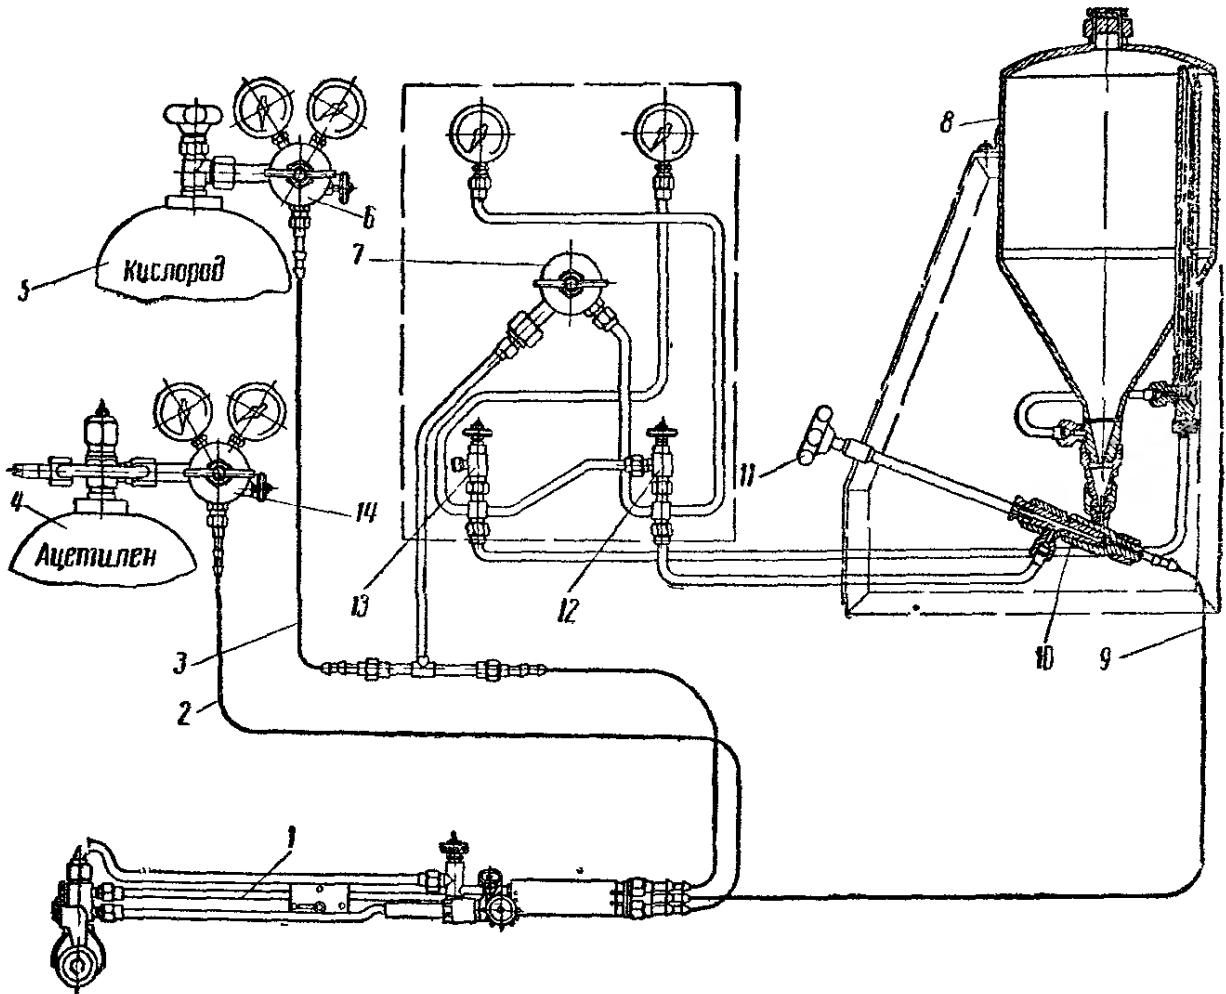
Схема установки УРХС для кислородно-флюсовой резки
